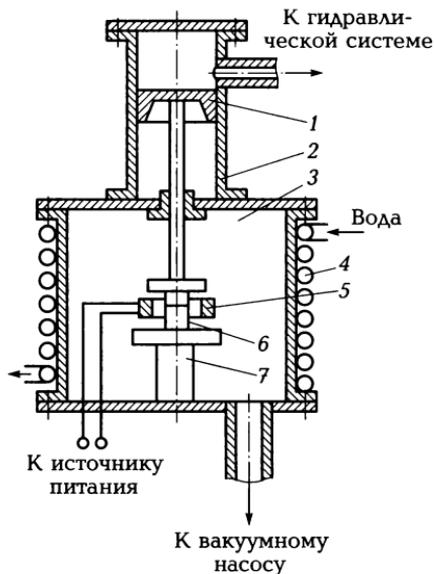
Схема диффузионной сварки в вакууме:
